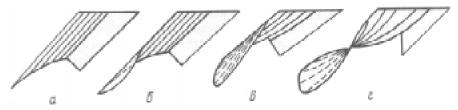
Виды рабочих поверхностей корпусов плуга: a — цилиндрическая; δ — культурная; ϵ — полувинтовая; ϵ — винтовая
